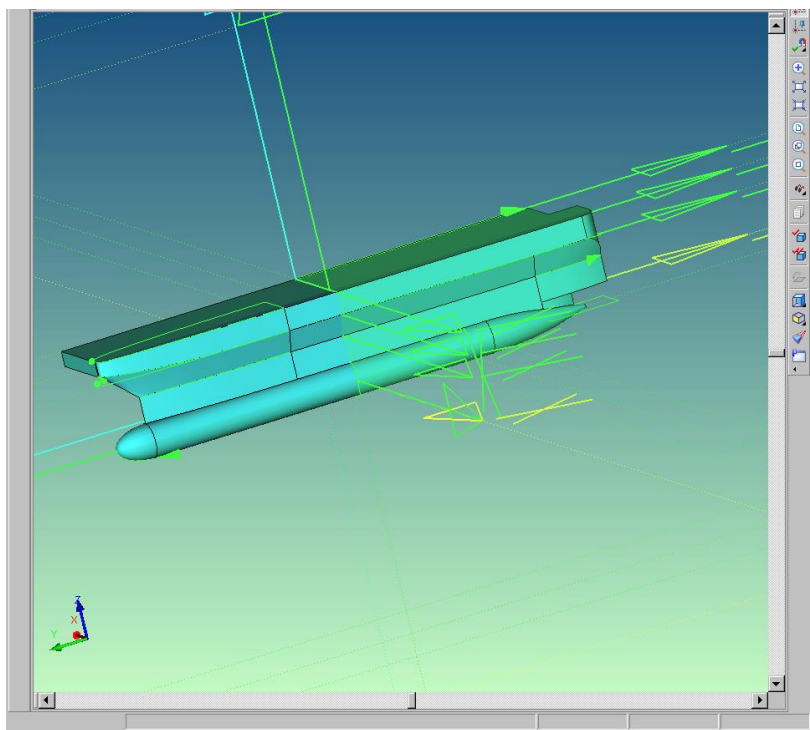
Конструювання 3D моделі корпусу СМПВ
